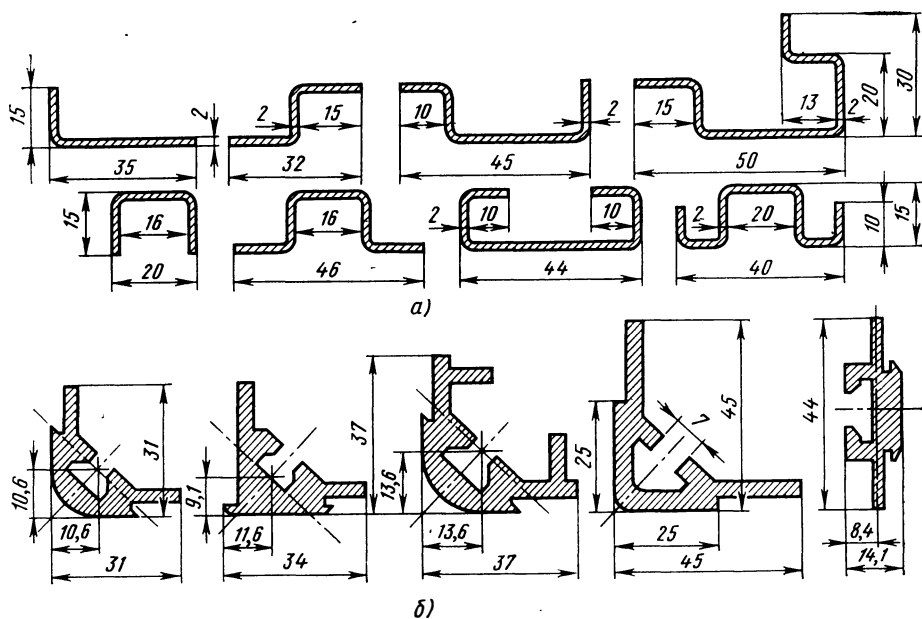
Балочные профили несущей конструкции, гнутые из тонколистового проката (а) и прессованные из алюминиевых сплавов (б)
